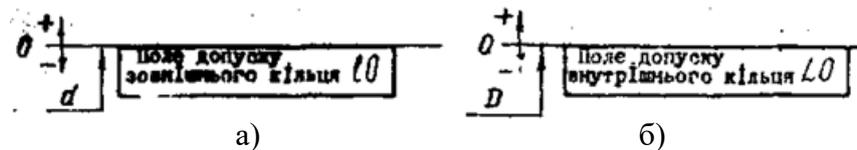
Поля допусків зовнішнього а) та внутрішнього б) кілець підшипника класу 0
